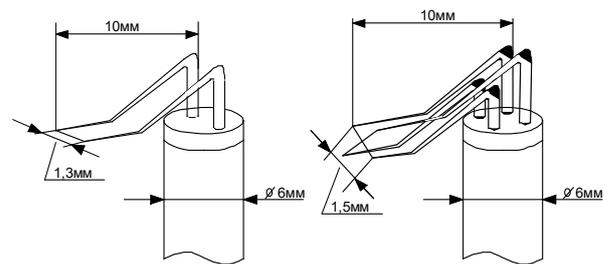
Конструкции датчиков термоанемометра с Г-образными ножками
